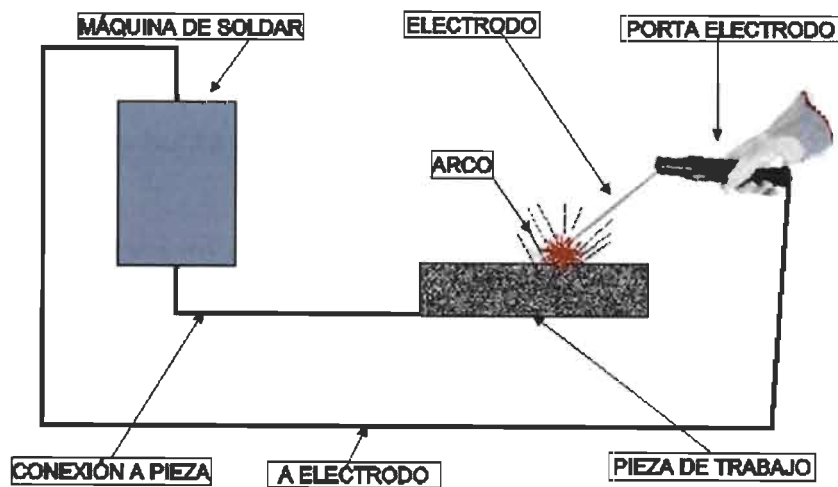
Elementos de un circuito de soldadura típico para SMAW (1).
